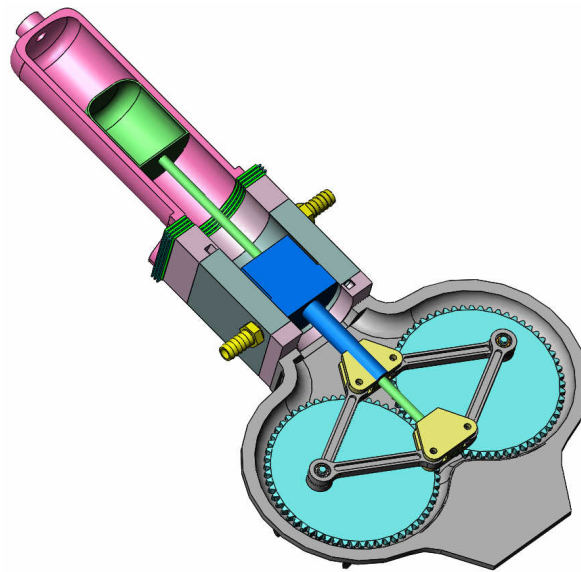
Motor Stirling Cinemático (Beta)[6]
